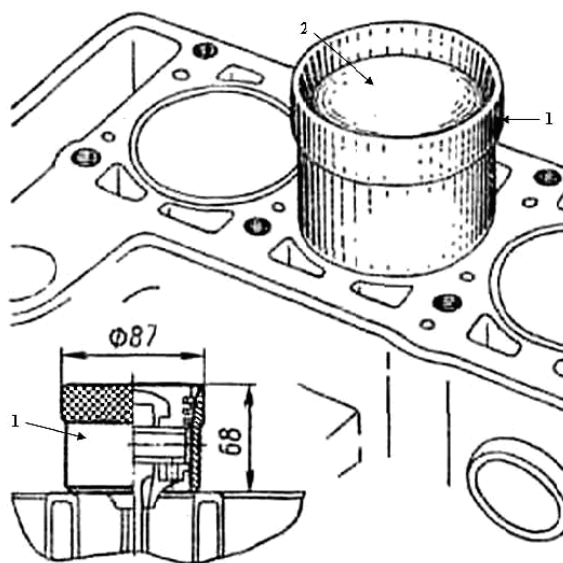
Установка поршня с поршневыми кольцами и шатуном в цилиндр двигателя при помощи оправки – обжима для колец:
